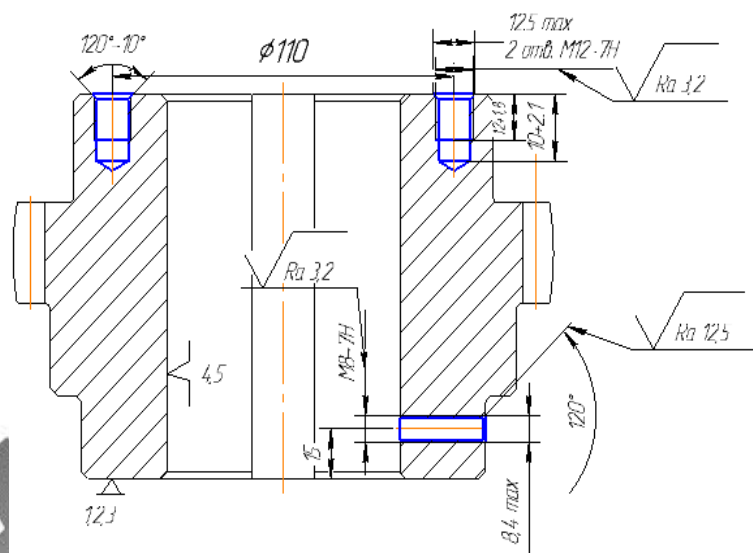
Схема базування деталі на операції 070 Свердлильній з ЧПК
